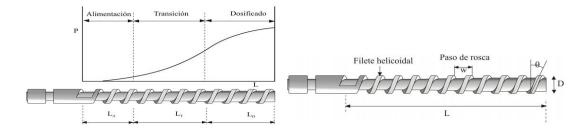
a) Zonas del tornillo. b) Tornillo de extrusión.
